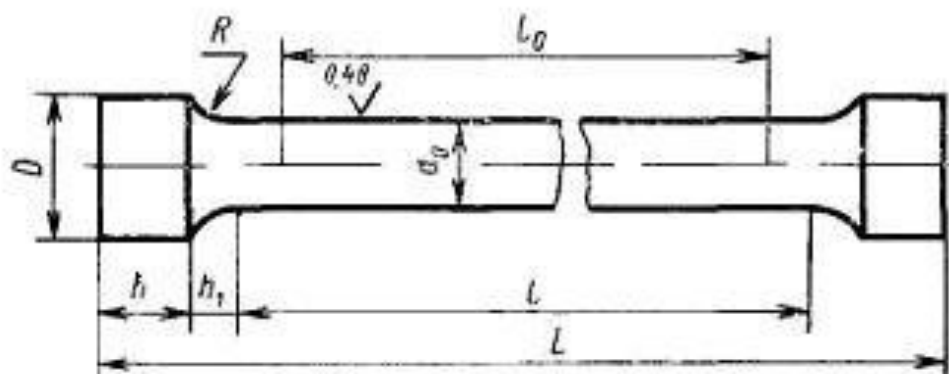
Образцы для испытаний, тип I, II, III
